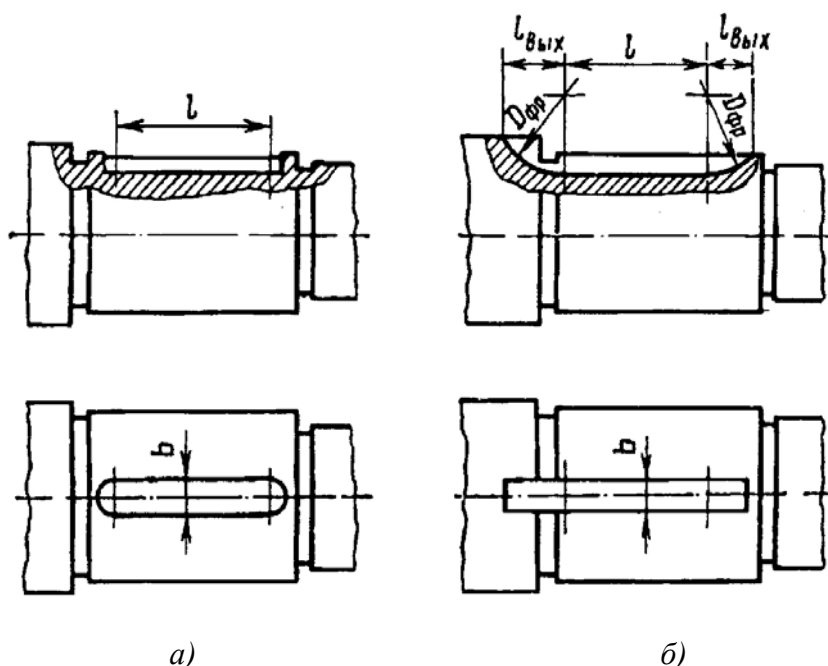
Шпоночные пазы при изготовлении: а - пальцевой фрезой; б - дисковой фрезой
